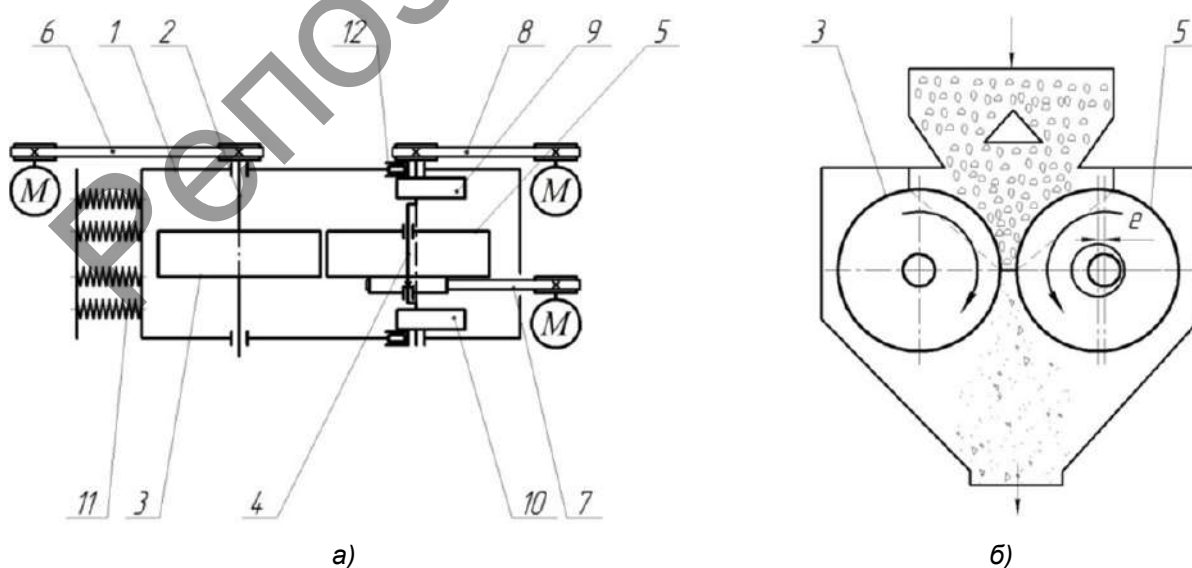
Схема вибровалкового измельчителя: а — вид сверху; б — вид сбоку
